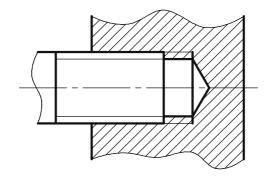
Разрез резьбового соединения с глухим резьбовым отверстием
